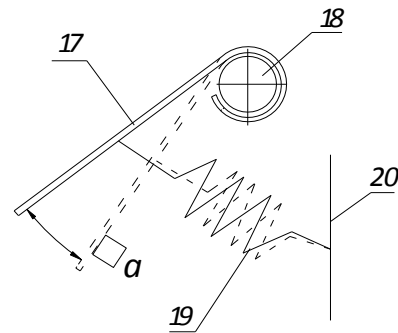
Пристрій для контролю виходу готового пакету з машини
